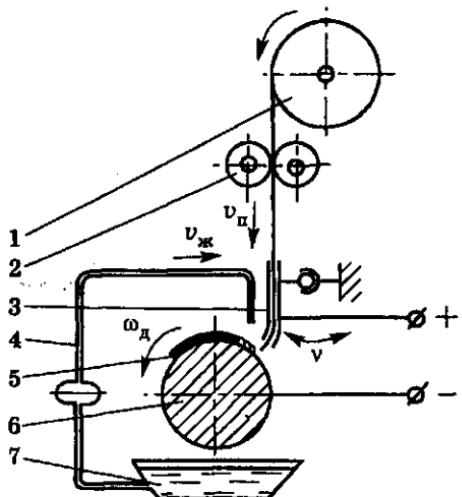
Схема вибродуговой наплавки: 1 — кассета для проволоки; 2 — ролики подающие; 3 — мундштук качающийся; 4 — система подачи раствора; 5 — наплавленный слой; 6 — восстанавливаемая деталь; 7 — емкость; v_n — скорость подачи проволоки; v_m — скорость подачи раствора; ω_d — угловая частота вращения детали; v — частота качаний мундштутка
